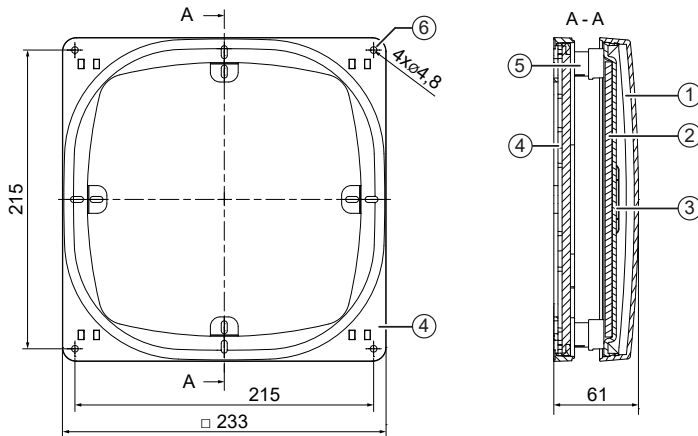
Maßzeichnung Innenblende Flair V-233x233
